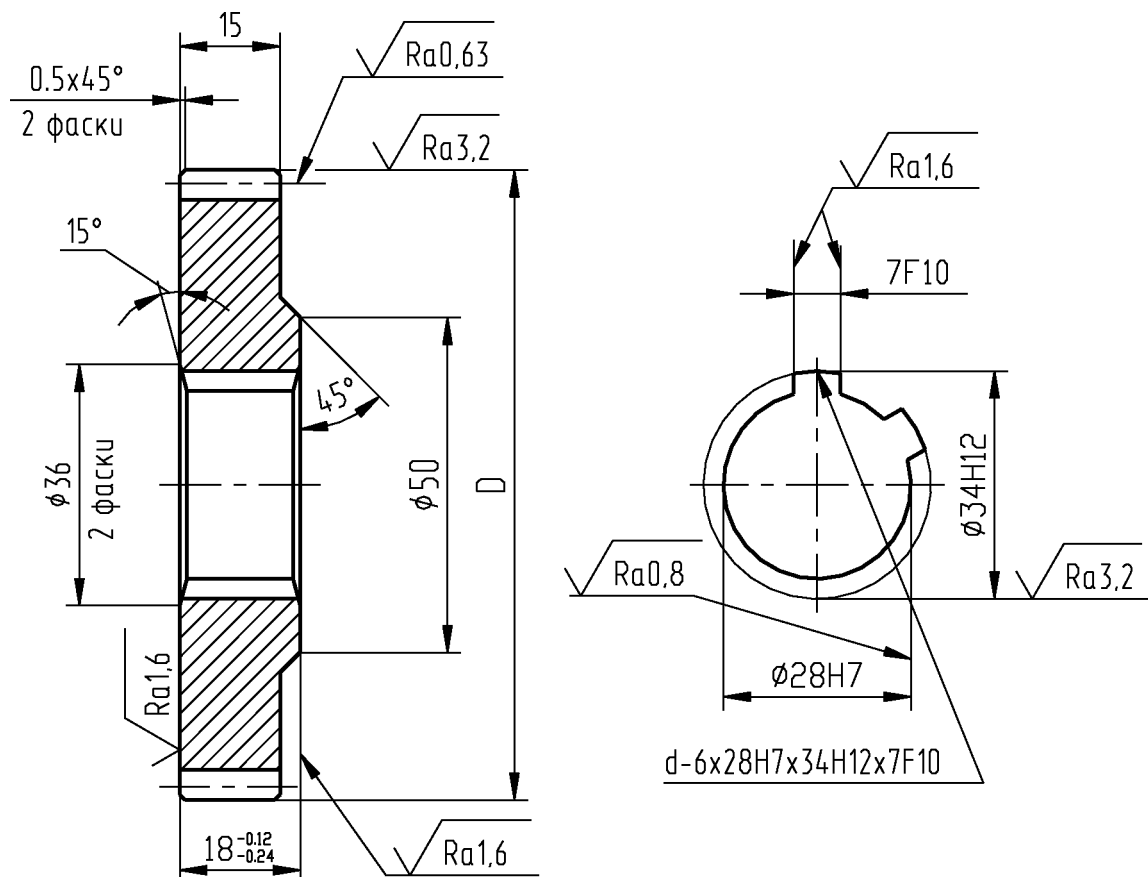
а - Типовой чертеж сменного зубчатого колеса
